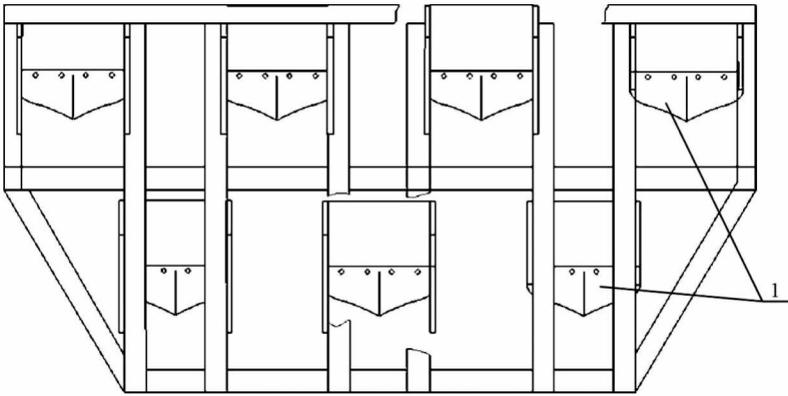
Схема устройства для создания полосы противопожарного назначения (вид сверху): 1 – культиваторные лапы в два ряда
